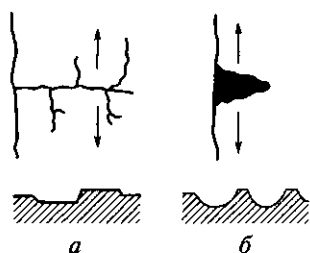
Вид трещины и схемы разрушения (сечение перпендикулярно поверхности излома):
